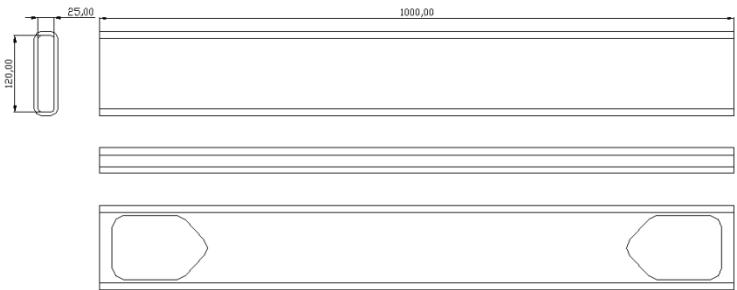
Bumper *reinforcement beam* B1 profil
